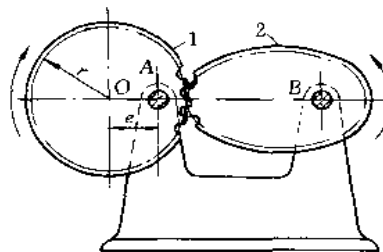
偏心圆齿轮-椭圆齿轮机构
